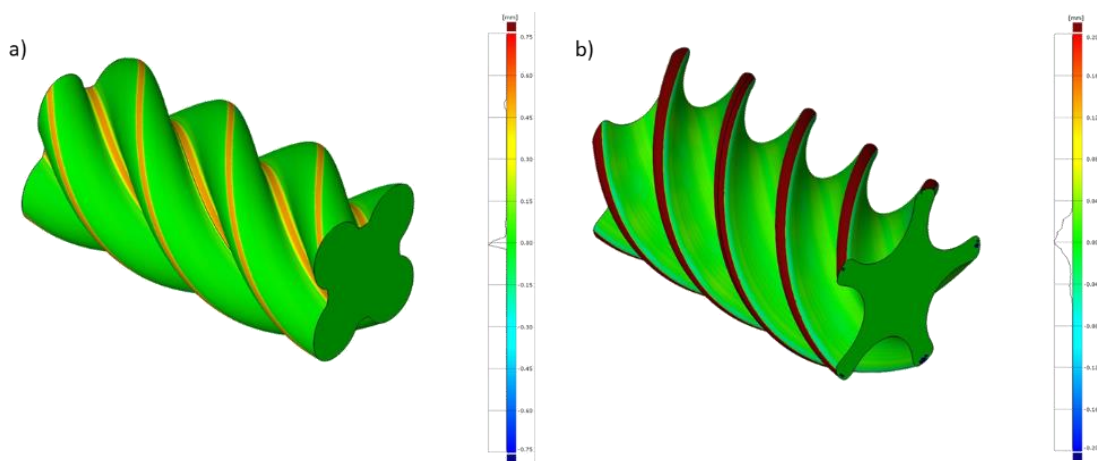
Desviación dimensional estimada del Demostrador III: a) Compresor de tornillo sin fin macho simétrico y b) Compresor de tornillo sin fin hembra simétrico.
